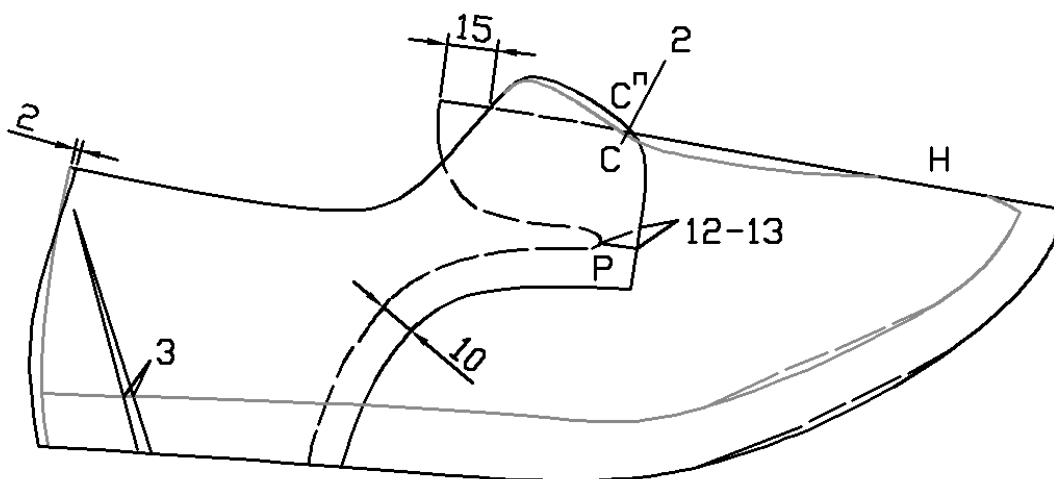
Конструктивная основа полуботинок с настрочными берцами «Дерби»
